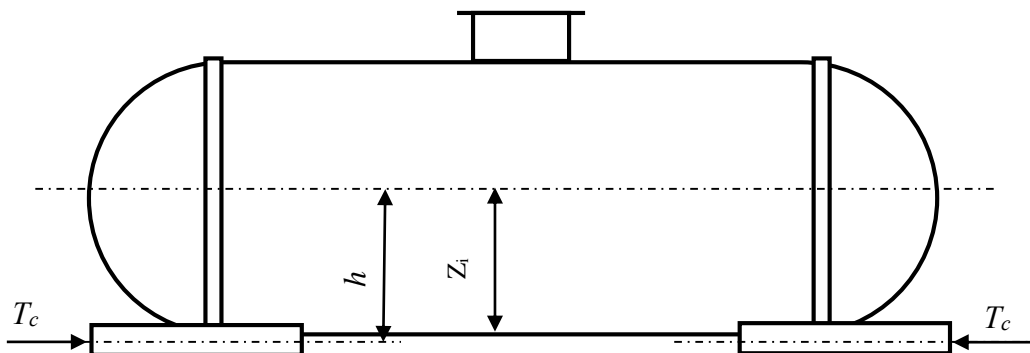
Расчетная схема котла на продольные нагрузки
